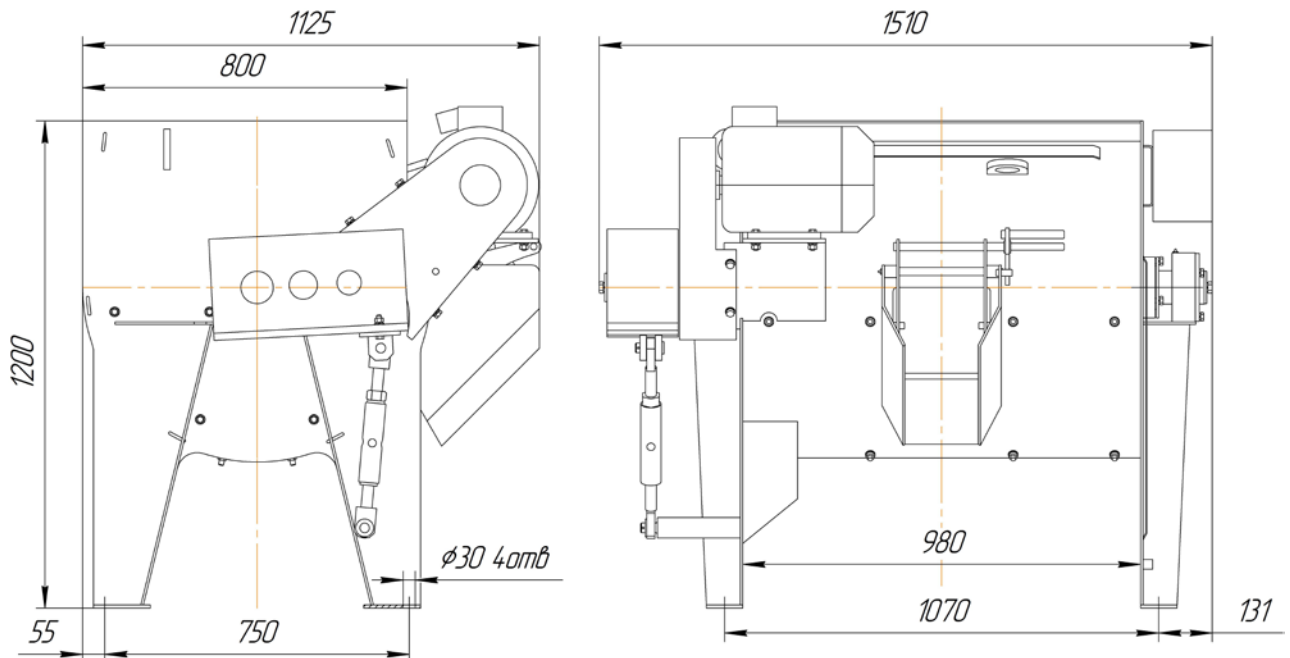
Габаритно-присоединительные размеры СГ-350.
